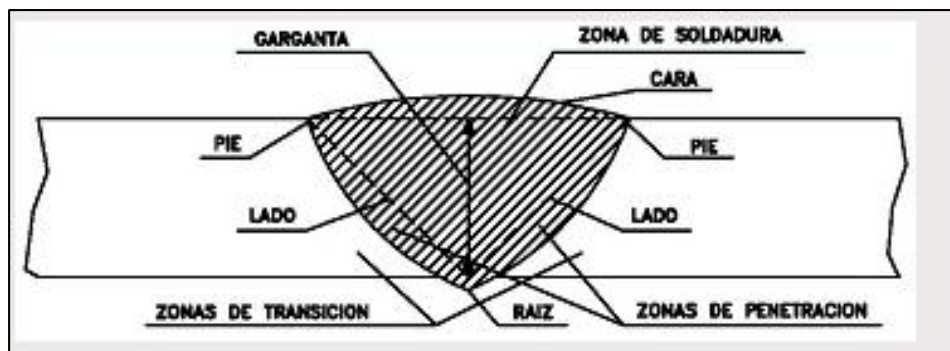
Partes de una unión con soldadura de arco eléctrico.
